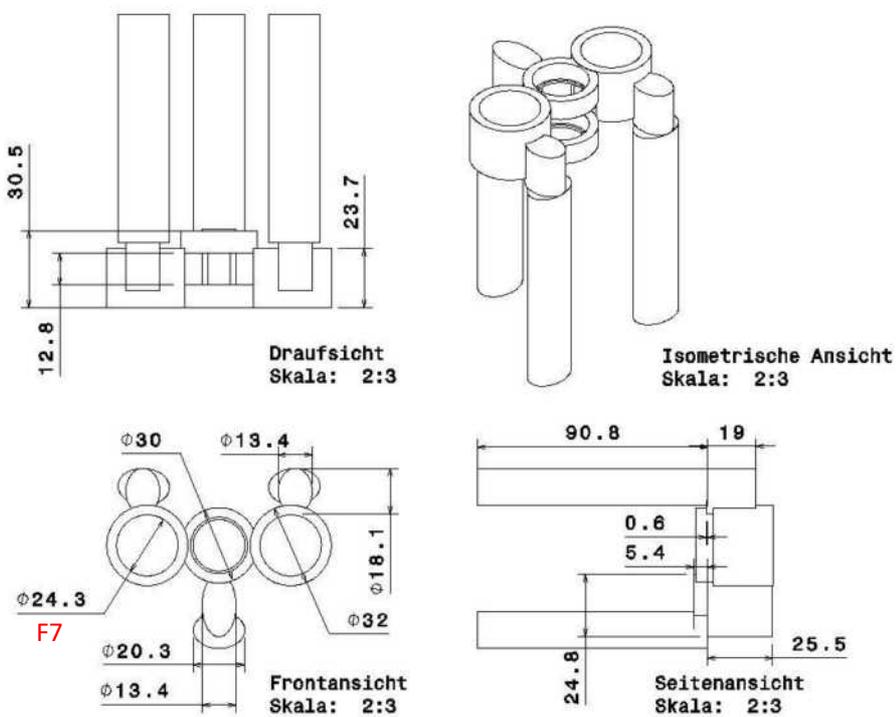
Element 2 (2D-Zeichnung) mit Toleranz Toleranz: fein.
